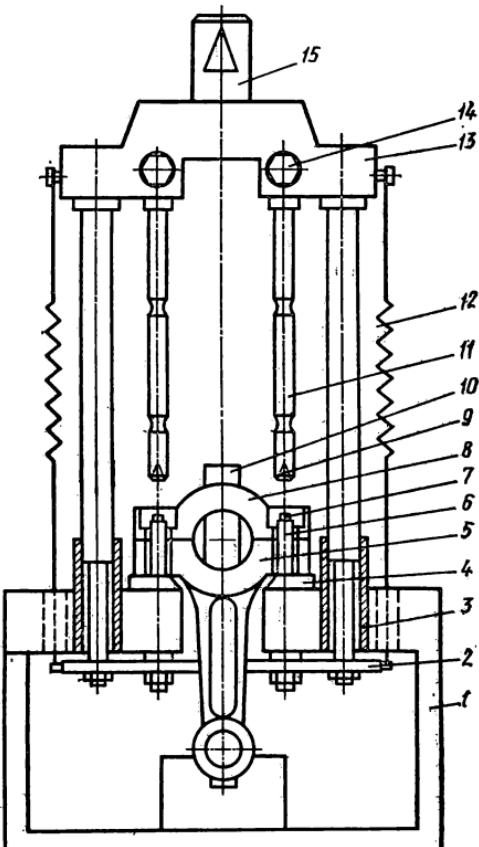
Координатно-прошивное приспособление для обработки отверстий в шатуне и крышке шатуна
